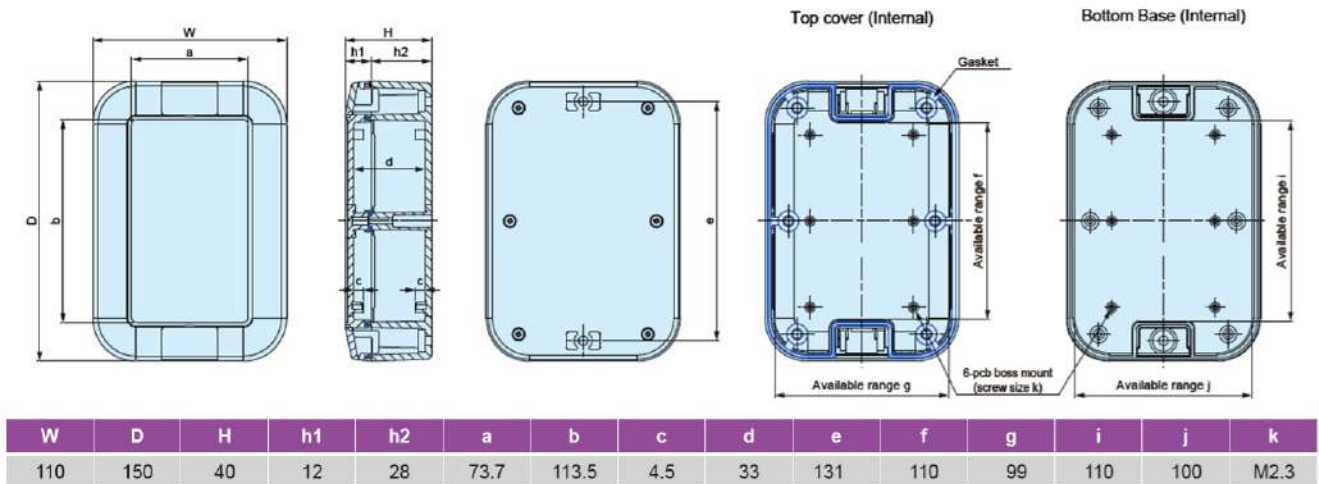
Dettaglio del fissaggio per la Meccanica del componente gateway della carrozzina
